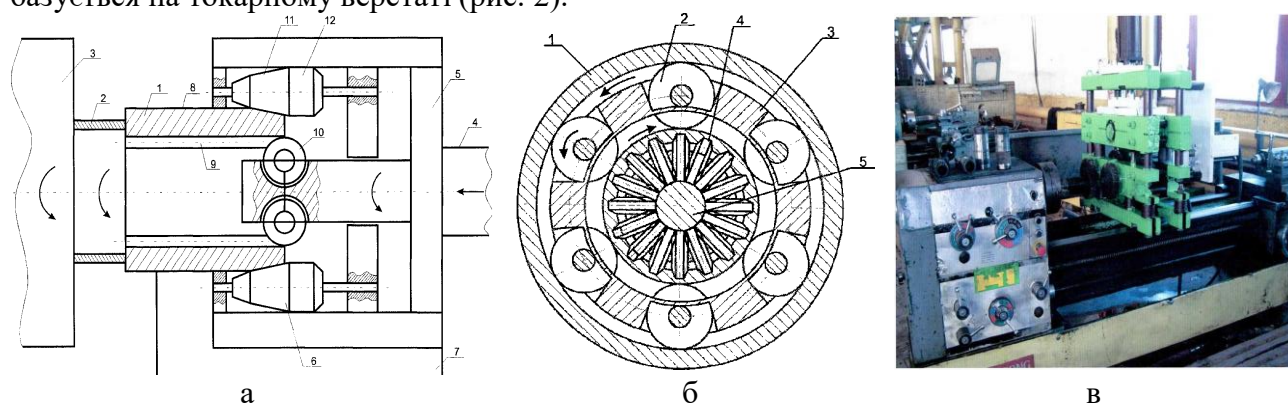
Пристрій для відновлення шліцевих втулок: а) - загальна схема; б) - схема конструкції накатної оснастки; в) - компонування пристрою на токарно-гвинторізному верстаті 16К20
